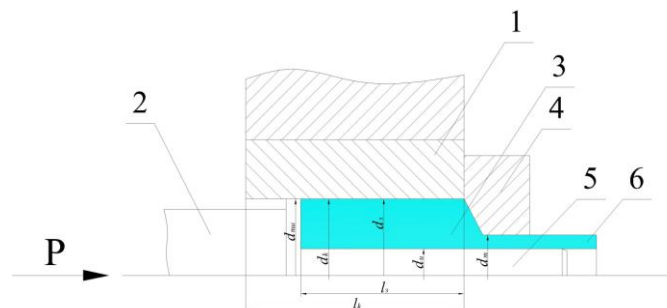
Схема прессования трубы: 1 – контейнер, 2 – пресс-штемпель с закрепленной пресс-шайбой, 3 – заготовка, 4 – матрица, 5 – игла, 6 – труба
